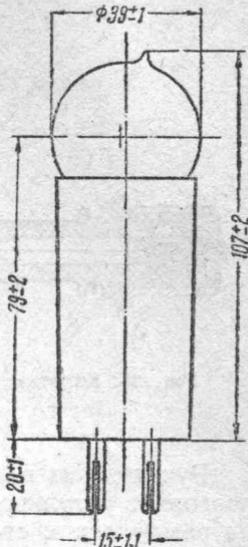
Общий вид и габаритные размеры фотоэлемента
